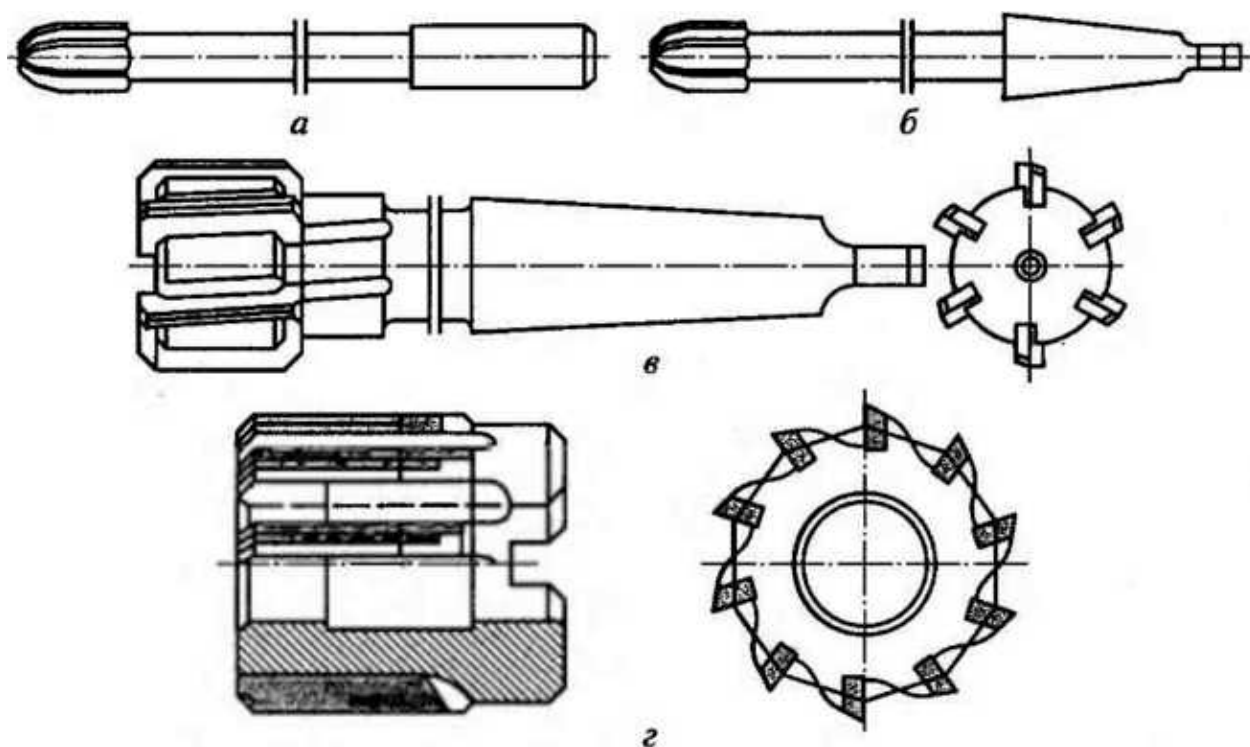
Развертки, оснащенные пластинами из твердого сплава:
